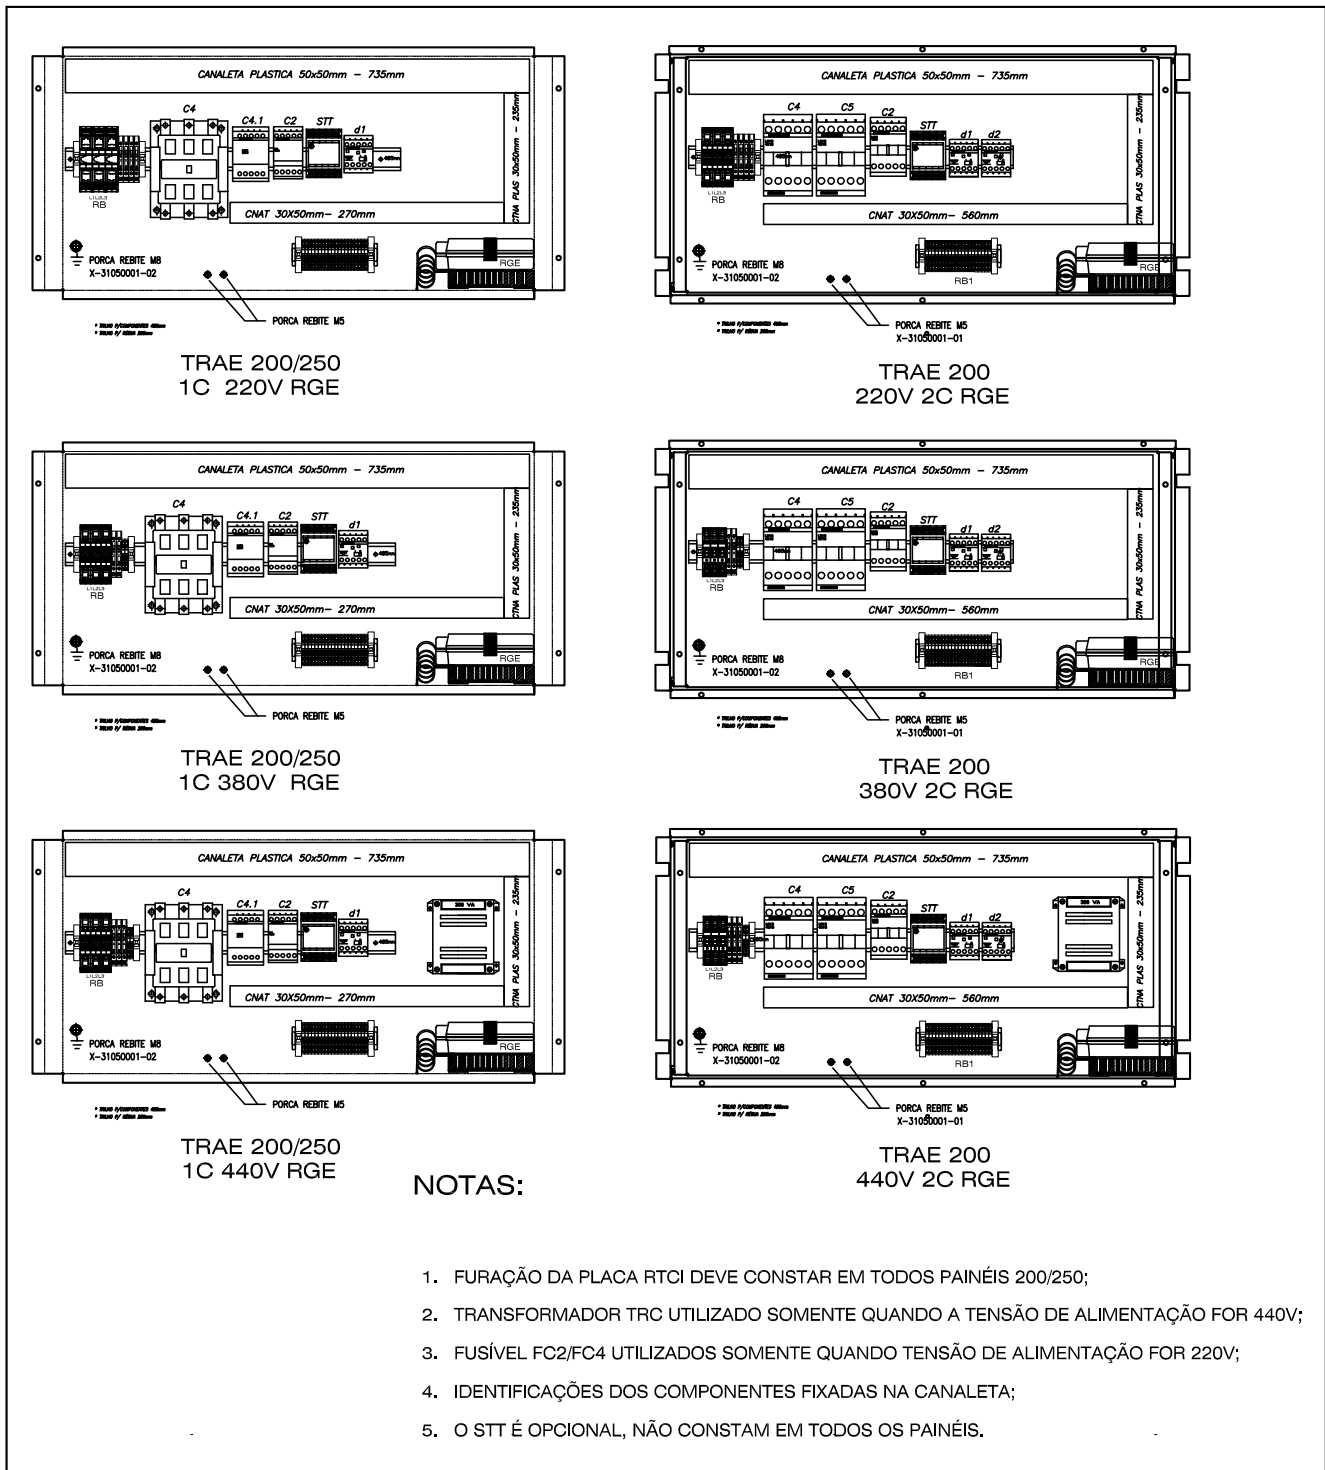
Lay Out de Tableros Eléctricos - TRAE (RGE)
